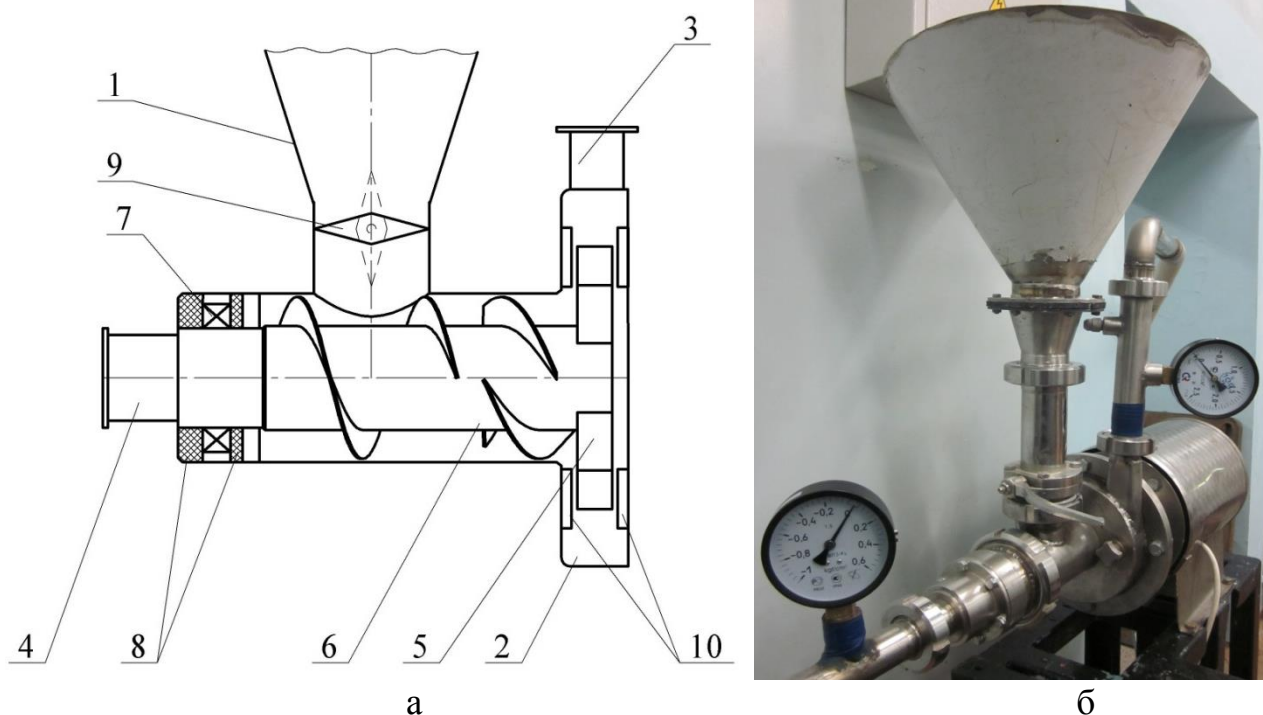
Схема (а) и общий вид (б) установки для приготовления жидких кормовых смесей
